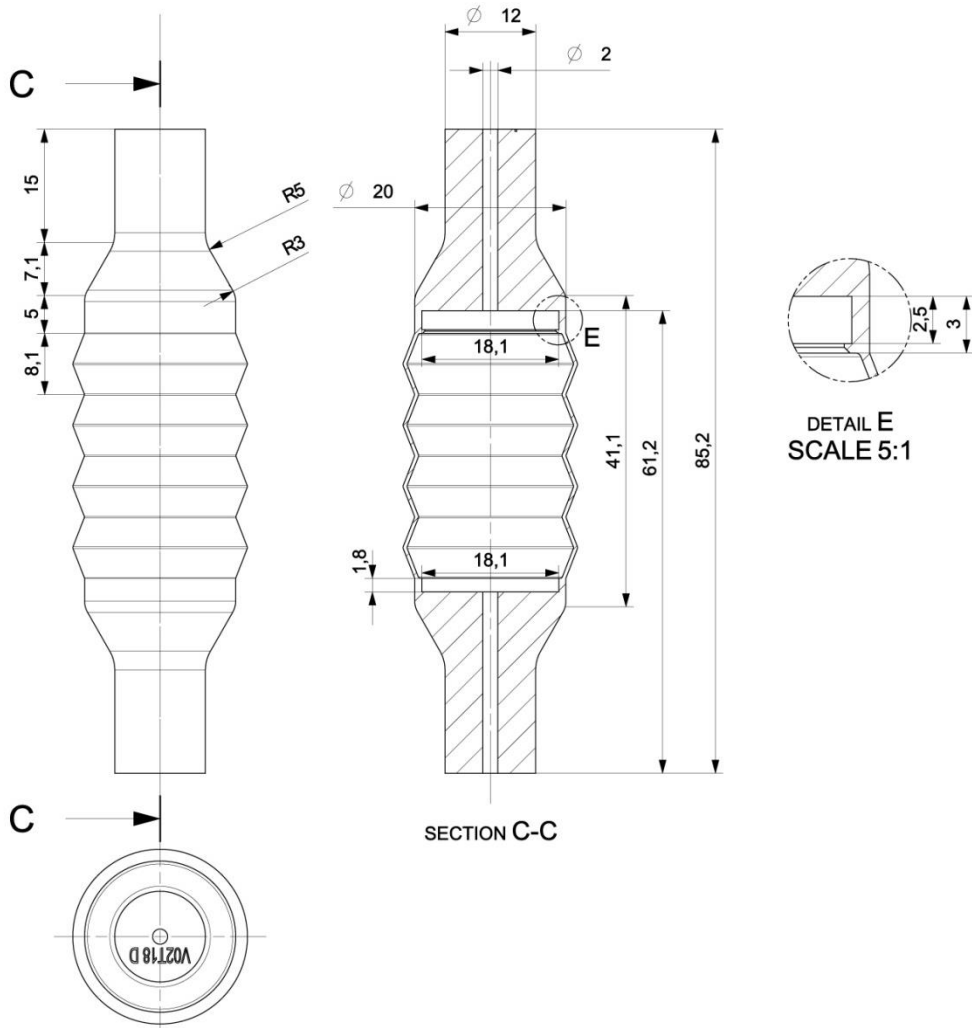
Technische Zeichnung Aktormodulgehäuse V02T18
